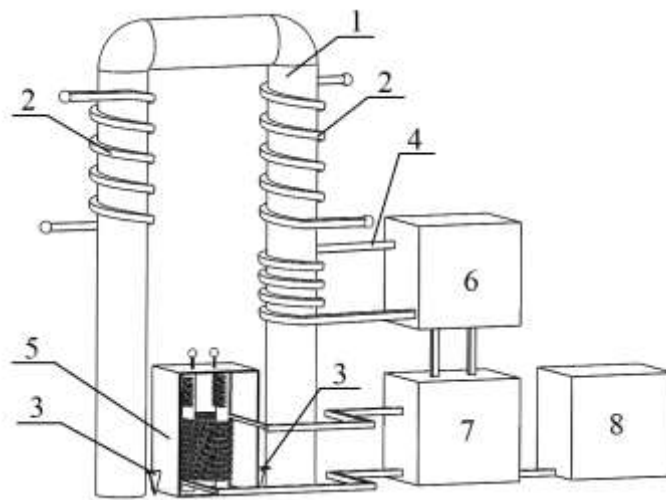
Пристрій для контролю механічних напружень в деталі,
